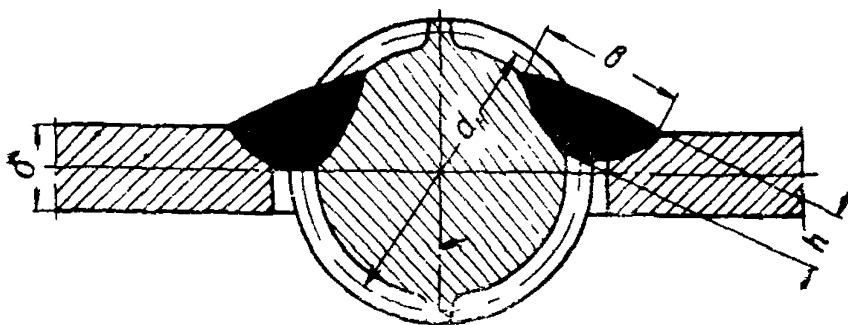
Схема измерения размеров сварных фланговых швов в тавровом (в плоскости) соединении стержня с плоскими элементами проката с прорезью
